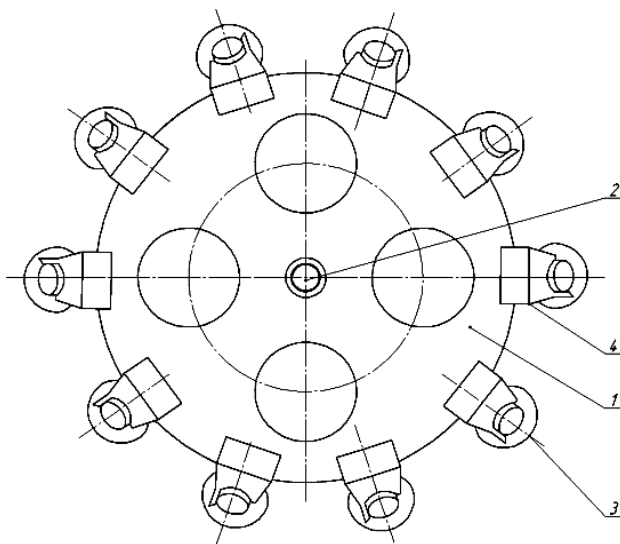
Навесное оборудование с рабочим инструментом в виде режущих дисков (вид сверху) 1 – диск, 2 – вал, 3 – дисковый резец, 4 – зубья
